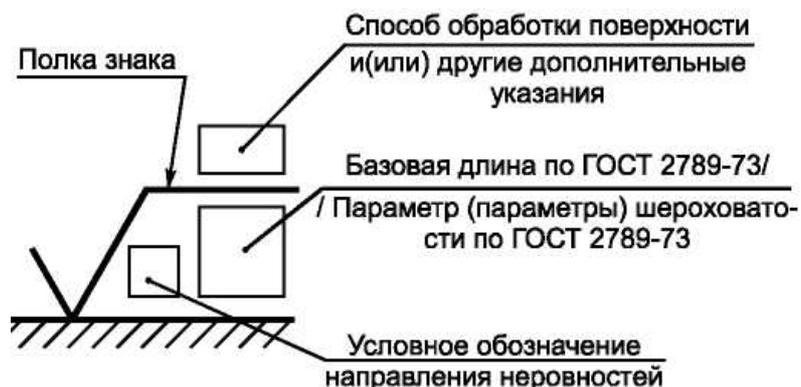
Структура обозначения шероховатости поверхности с указанием параметров шероховатости и способа обработки поверхности
